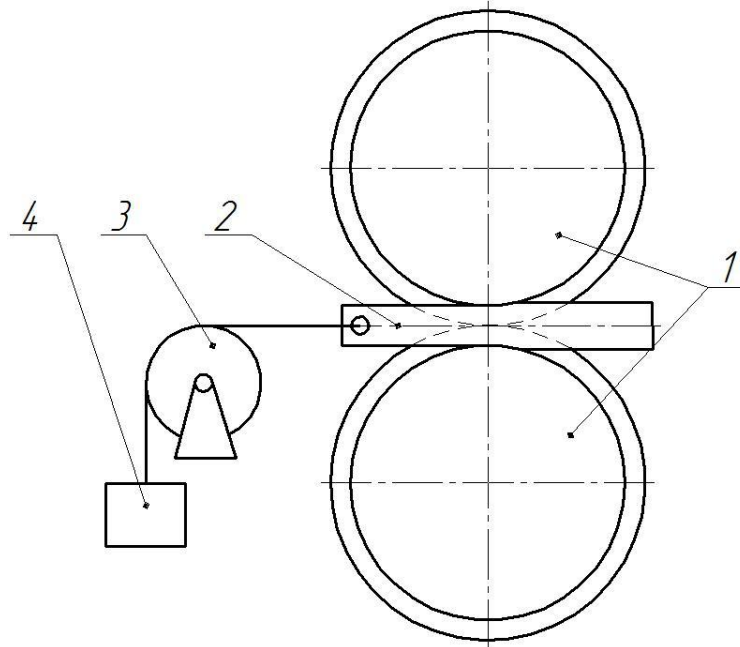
Схема установки: 1 – прокатные валки; 2– деформируемая заготовка; 3 – блок; 4 – груз
